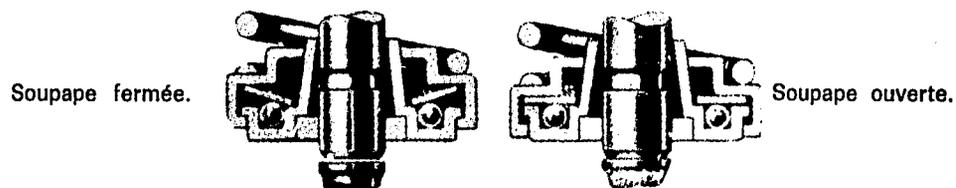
Un dispositif rotatif de soupapes du type positif fait légèrement tourner la soupape chaque fois qu'elle se soulève
